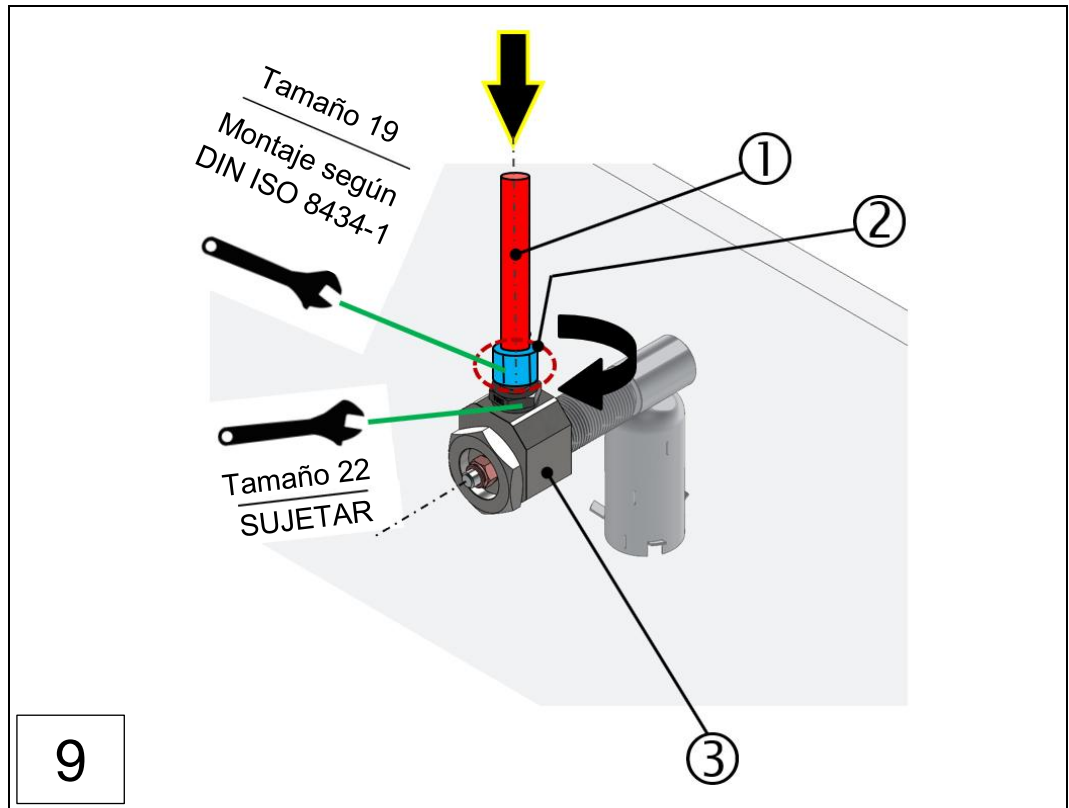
Proceso de montaje, conexión a la pared del motor VN2020 (pasos de montaje 1-9)
